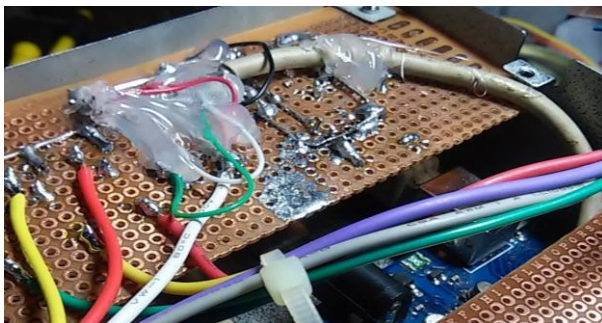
Detalhe do cabo USB soldado na placa de controle cabos fixados e protegidos com cola quente.
